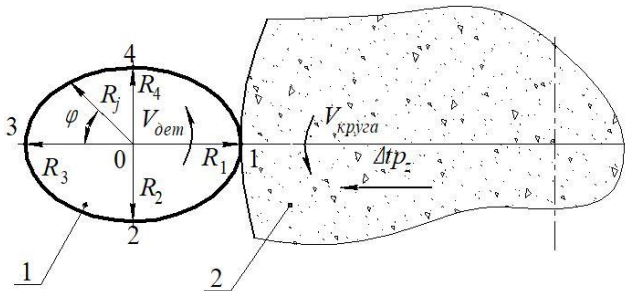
Начало процесса шлифования с момента касания круга наибольшим радиусом R_1 эллипсной заготовки: 1 – заготовка с эллипсным профилем; 2 – шлифовальный круг
